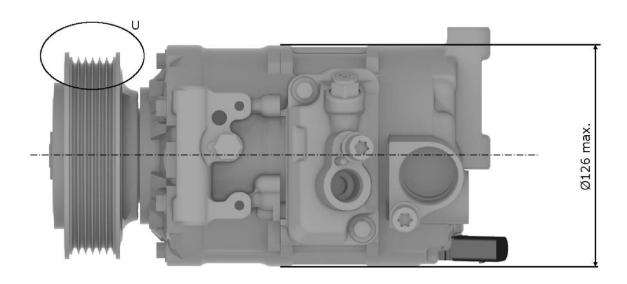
Dimensions du compresseur de climatiseur (vue de dessus)
